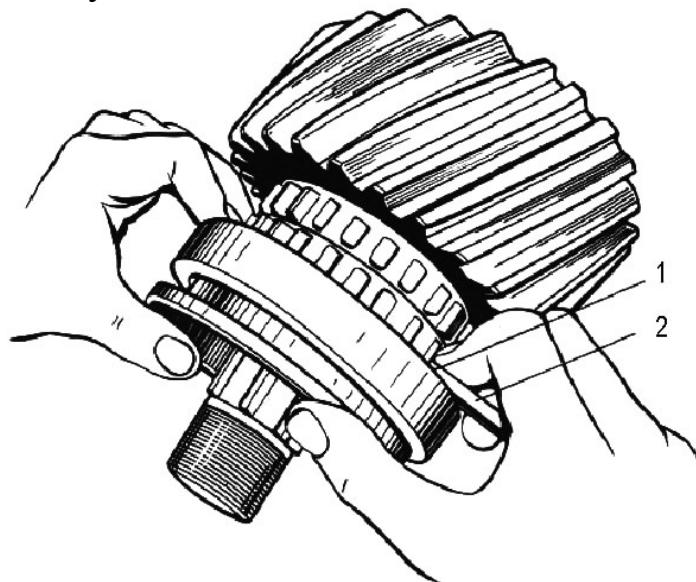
Установка пружин и шариков-фиксаторов муфты блокировки дифференциала:
